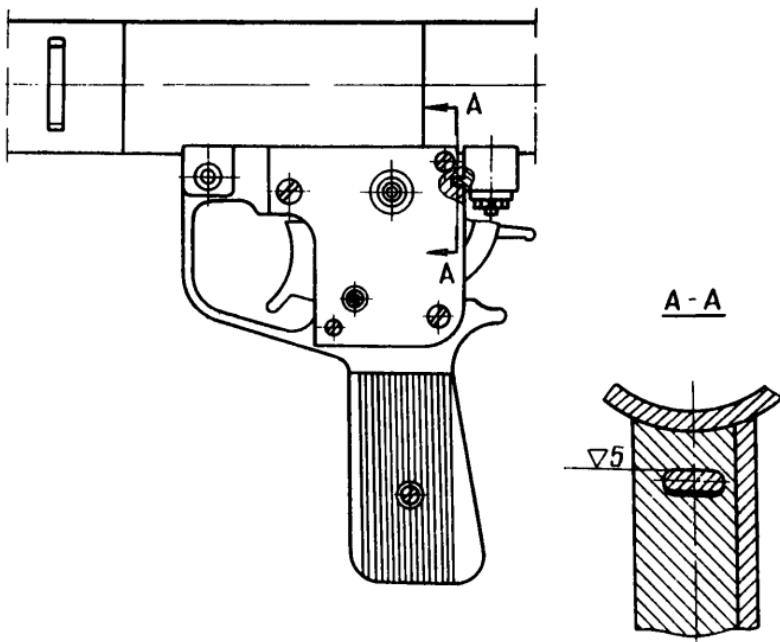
Подгонка выступа на основании бойка к корпусу ударно-спускового механизма
